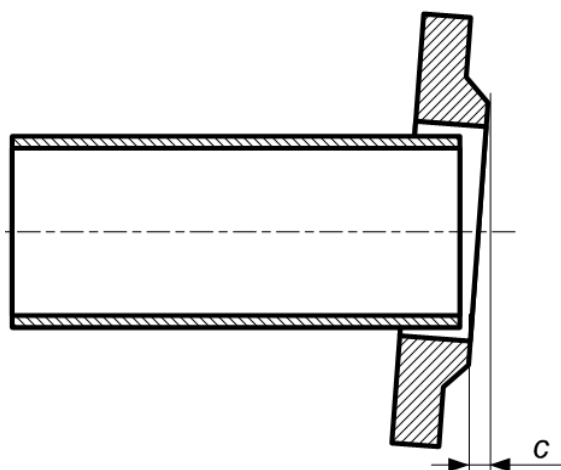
Сварка фланцев с прямыми отрезками трубопровода.
